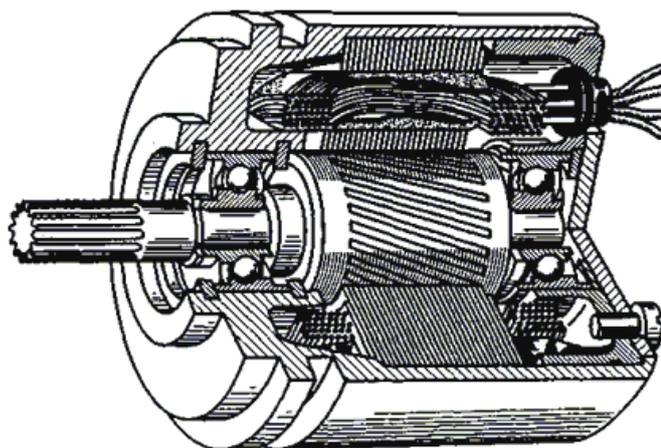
Асинхронный исполнительный двигатель сквозной конструкции
